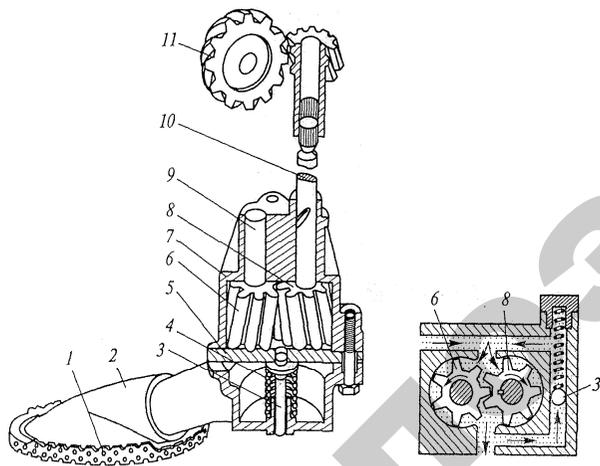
Масляный насос с шестернями наружного зацепления:
